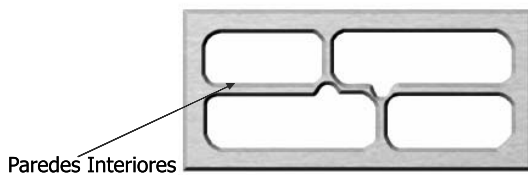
Conjugación de paredes. Fuente: Hitchiner Manufacturing Co., Inc. Designing for investment casting, Technical Updated 2D1.
